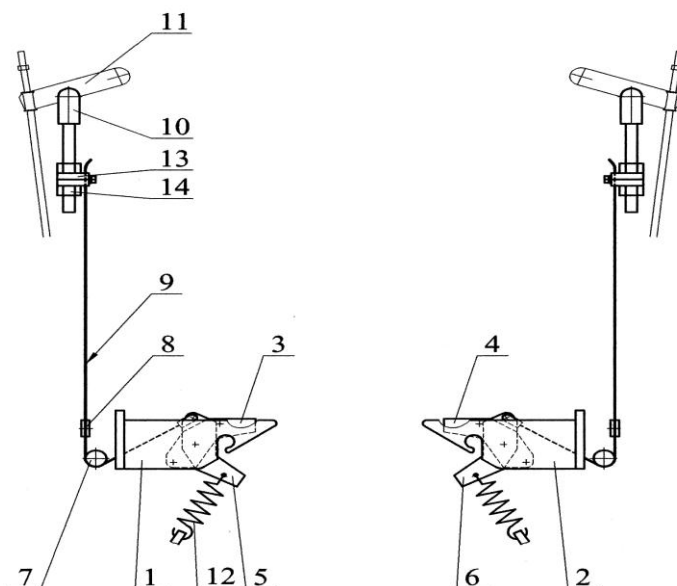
Регулировка натяжения пружин гидромеханического балансира
